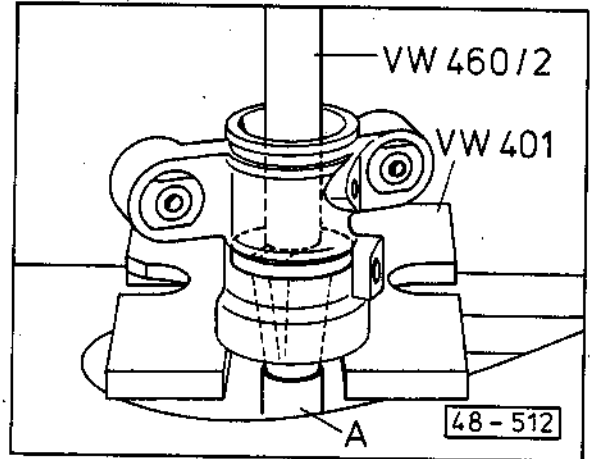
Dichtring mit Lagerring aus Gehäuse ausziehen
